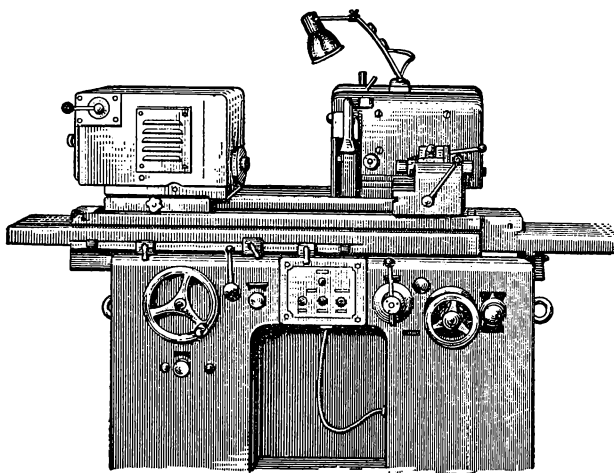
Общий вид универсального круглошлифовального станка 312М
